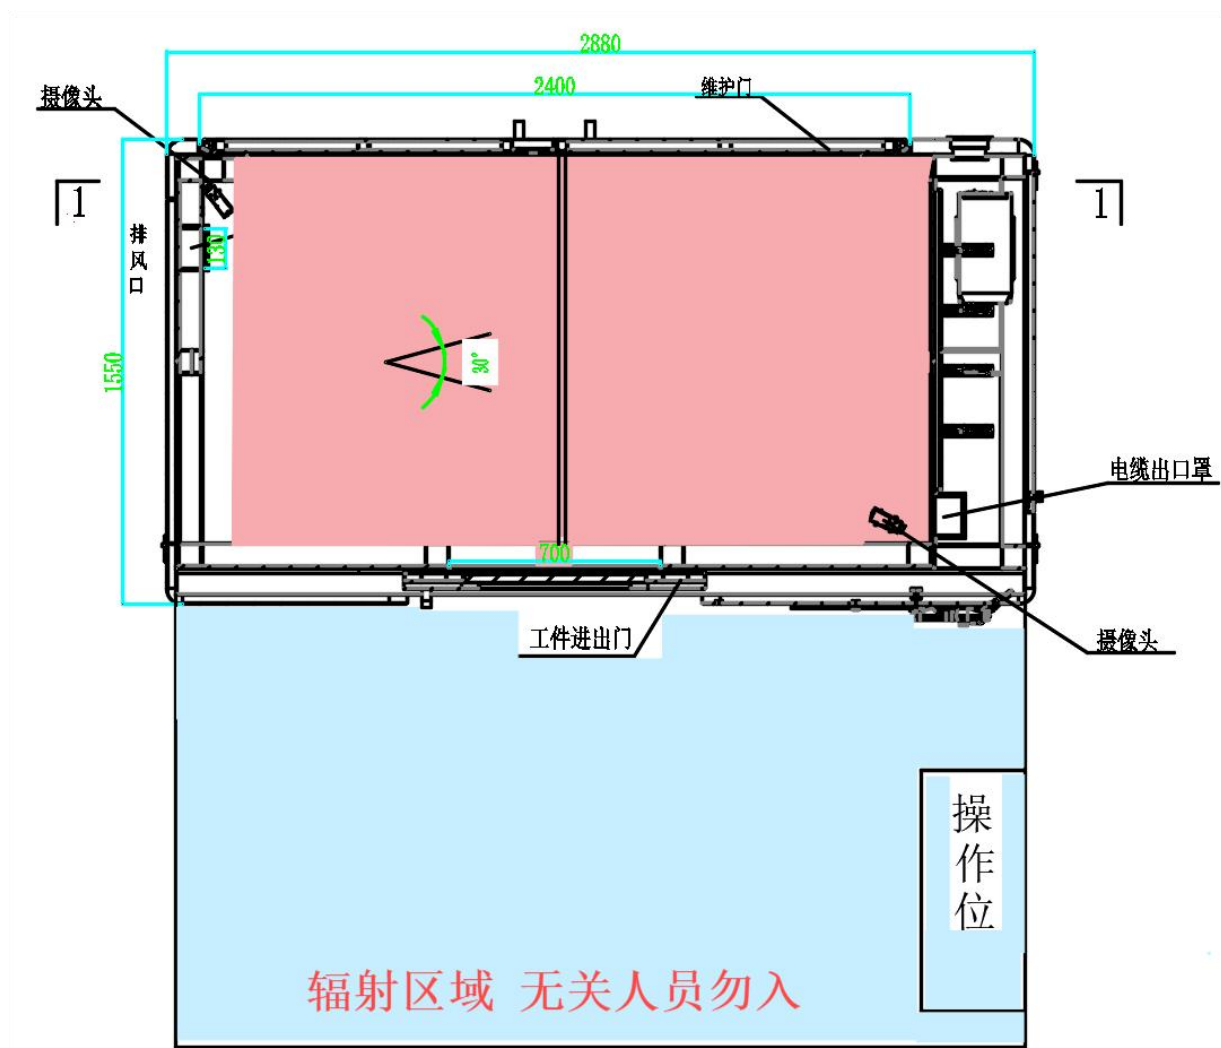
(a) AL-CT-225 型工业 CT 机辐射屏蔽室平面布置示意图 (mm)
